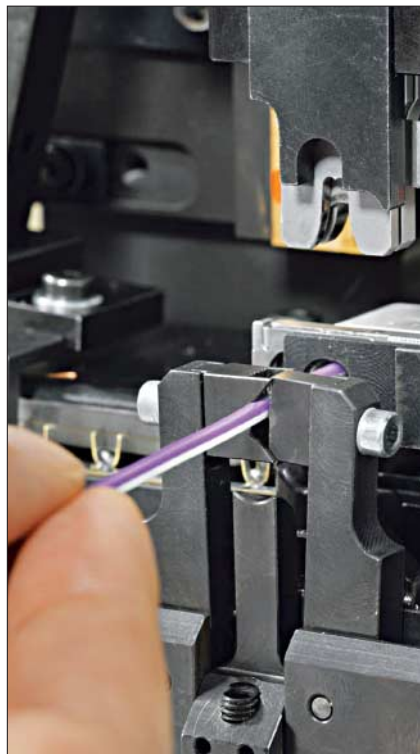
Kabelbearbeitung mit einer Strip Crimp 200
